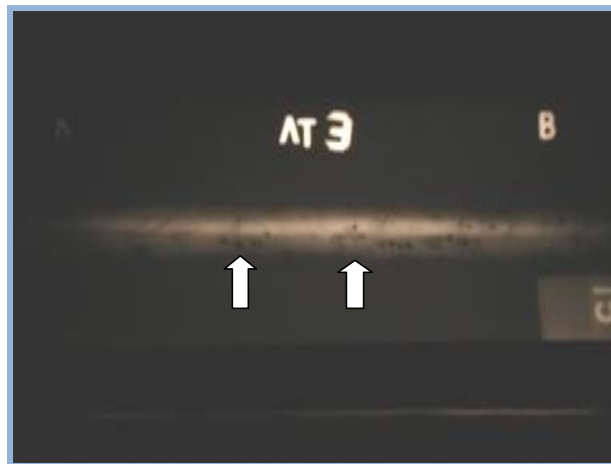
, Probeta N° 03: Fisuras Transversales.
